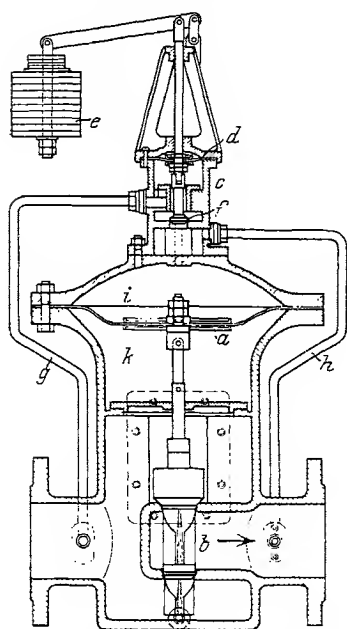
Membran-Umlaufregler mit Steuerregler der J. PINTSCH A. G., Berlin.
